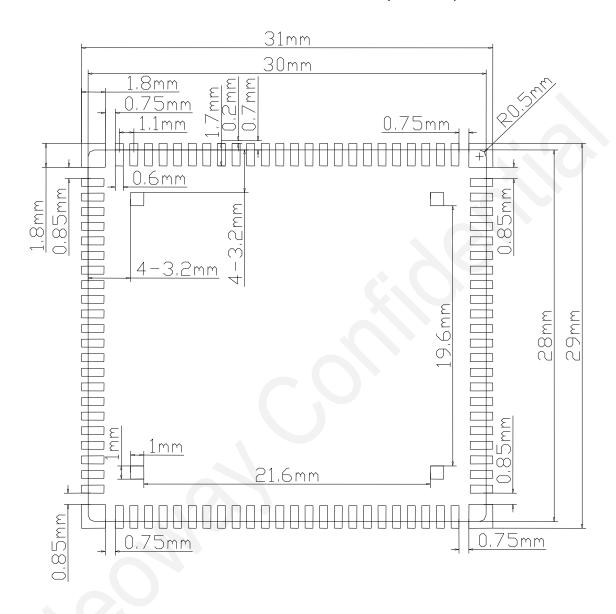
N720V5 模块 PCB 封装底视图(单位: mm)
